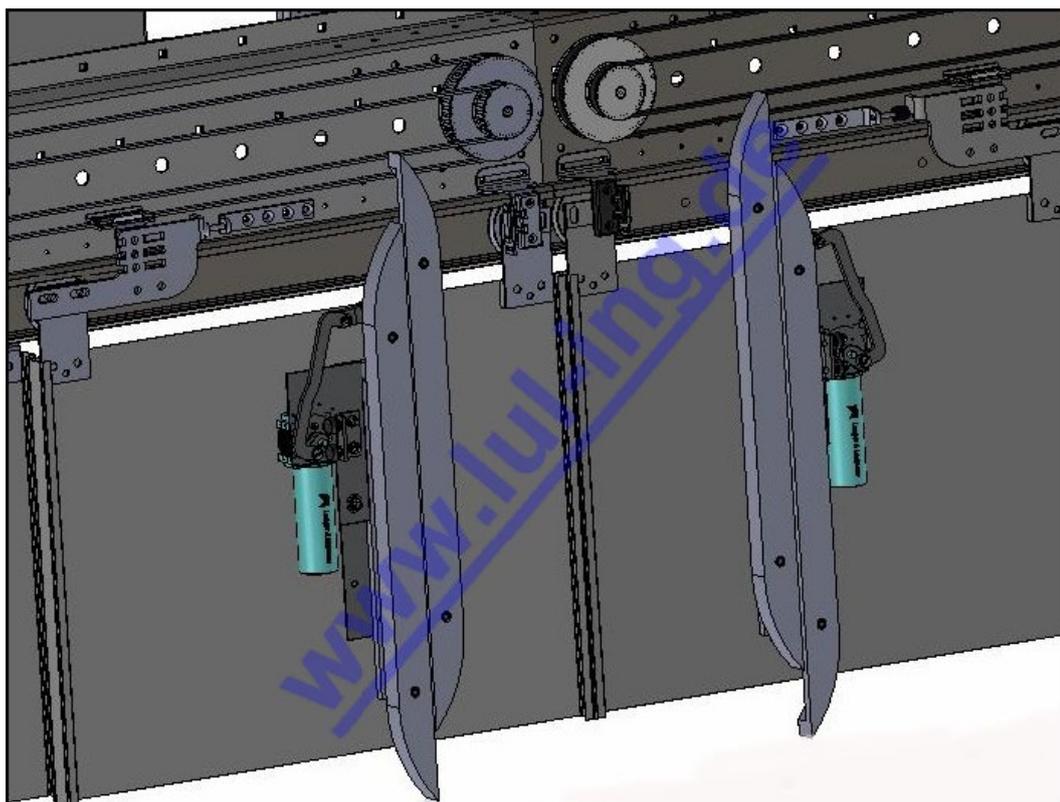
Machine de porte L&L QKS10 – Vue en 3D
